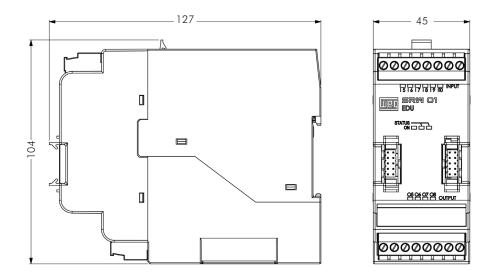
Dimensiones Unidad Expansión Digital - EDU (mm)
